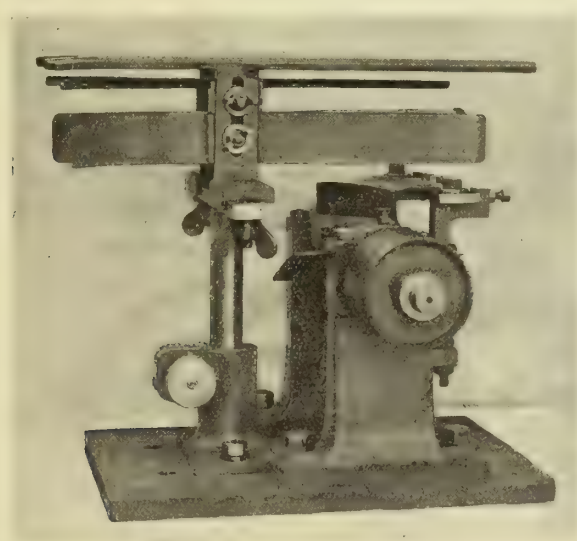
Fig. C. — Vue perspective des dispositions de la machine de M. H. Vollet.
